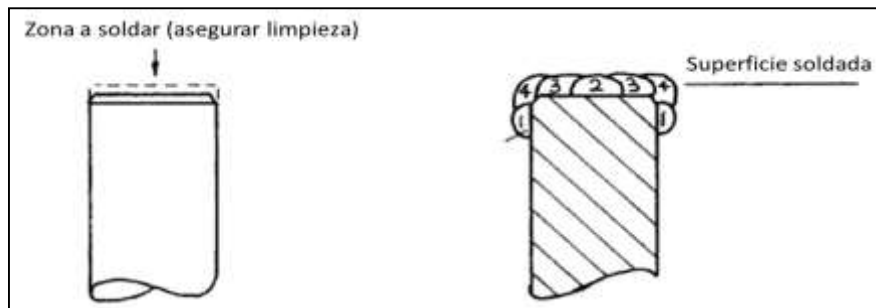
8 Representación de método a soldar cuando se presenta desgaste en un molde (16)
